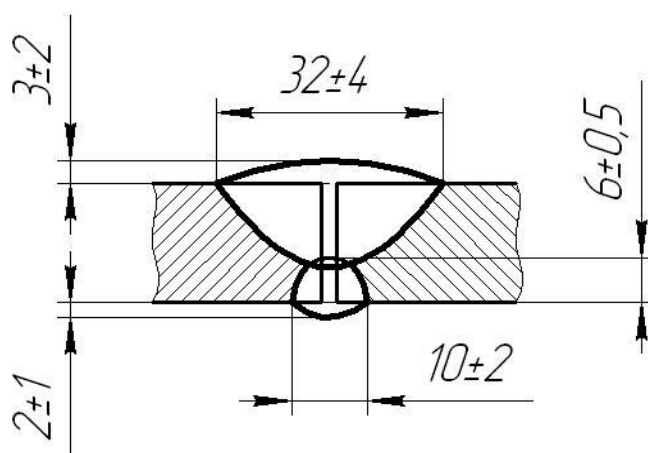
Геометрические параметры сварного шва после автоматической сварки под флюсом
